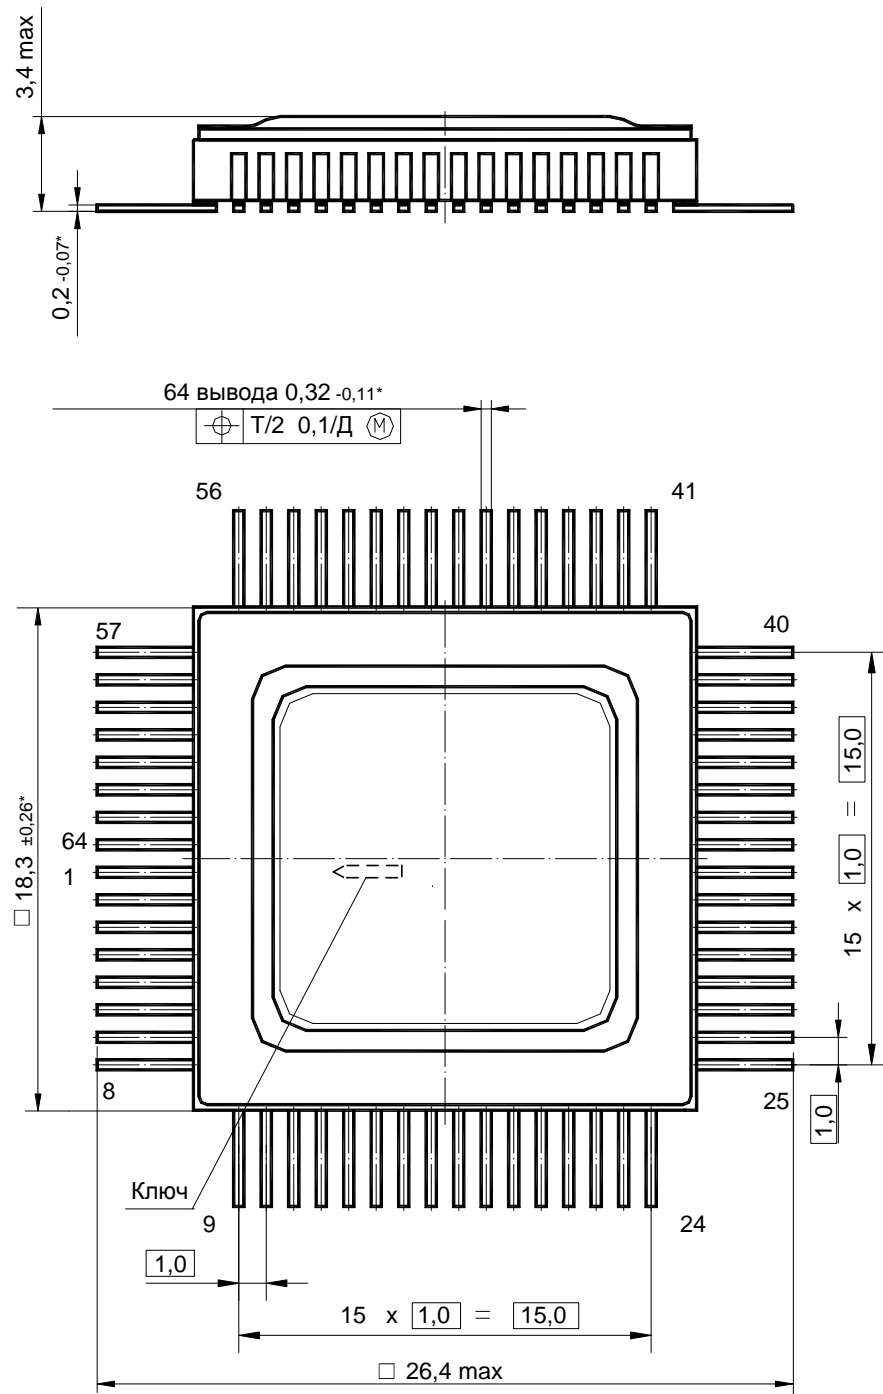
Габаритный чертеж корпуса 5134.64-6
